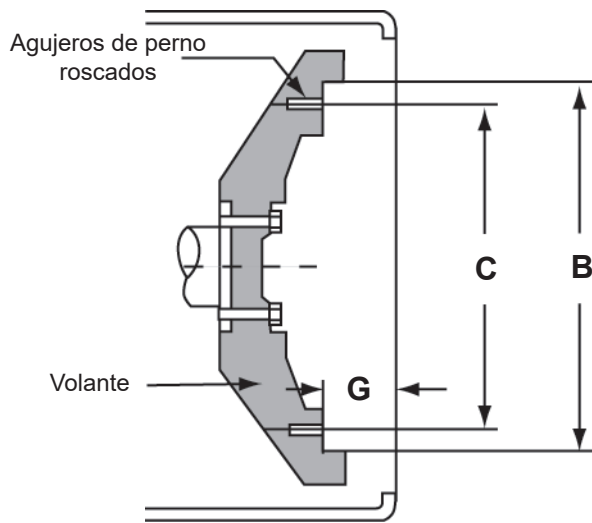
Plato de transmisión y adaptador de un solo cojinete
